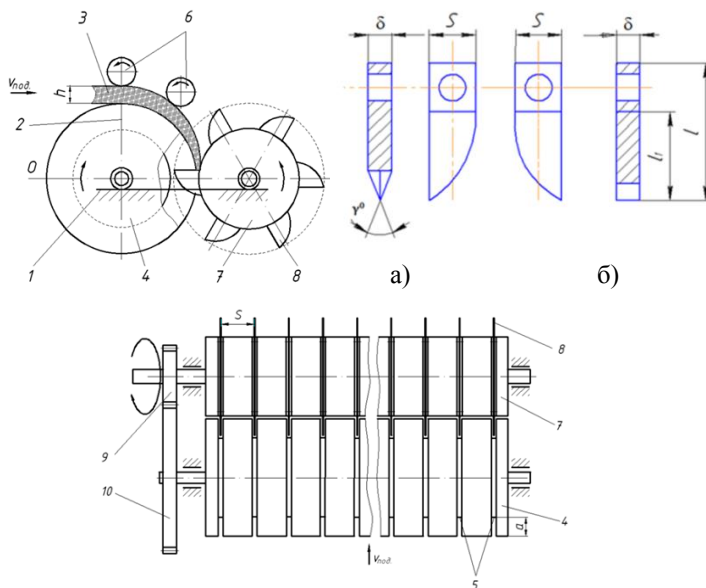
Схема пристрою для руйнування стебел льону олійного: 1 – корпус; 2 – шароформував; 3 – шар стебел; 4 – подавальний барабан; 5 – щілини – протирізи; 6 – притискні вальці; 7 – ротор; 8 – ножі(а) різального; б) молоткового типу); 9 – ведуча шестерня; 10 – зубчасте колесо
